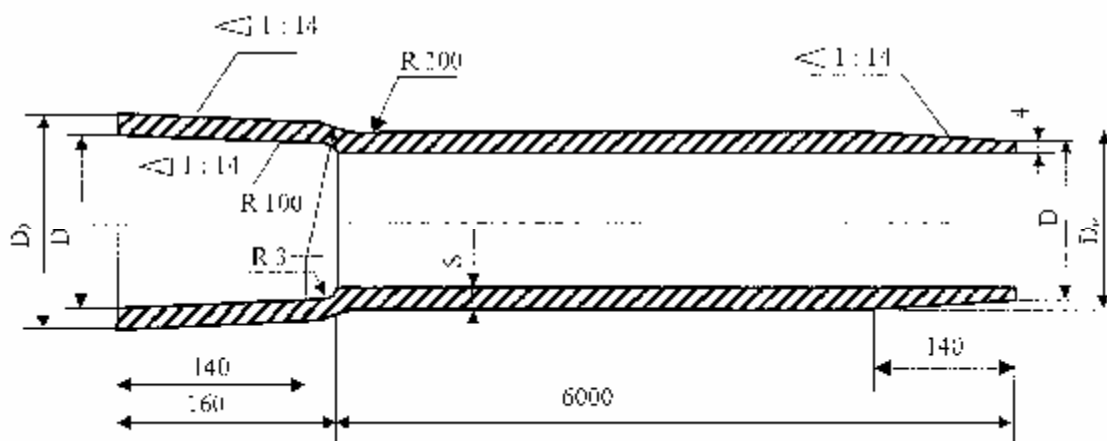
П1. Схема трубы под нахлестное сварное соединение
